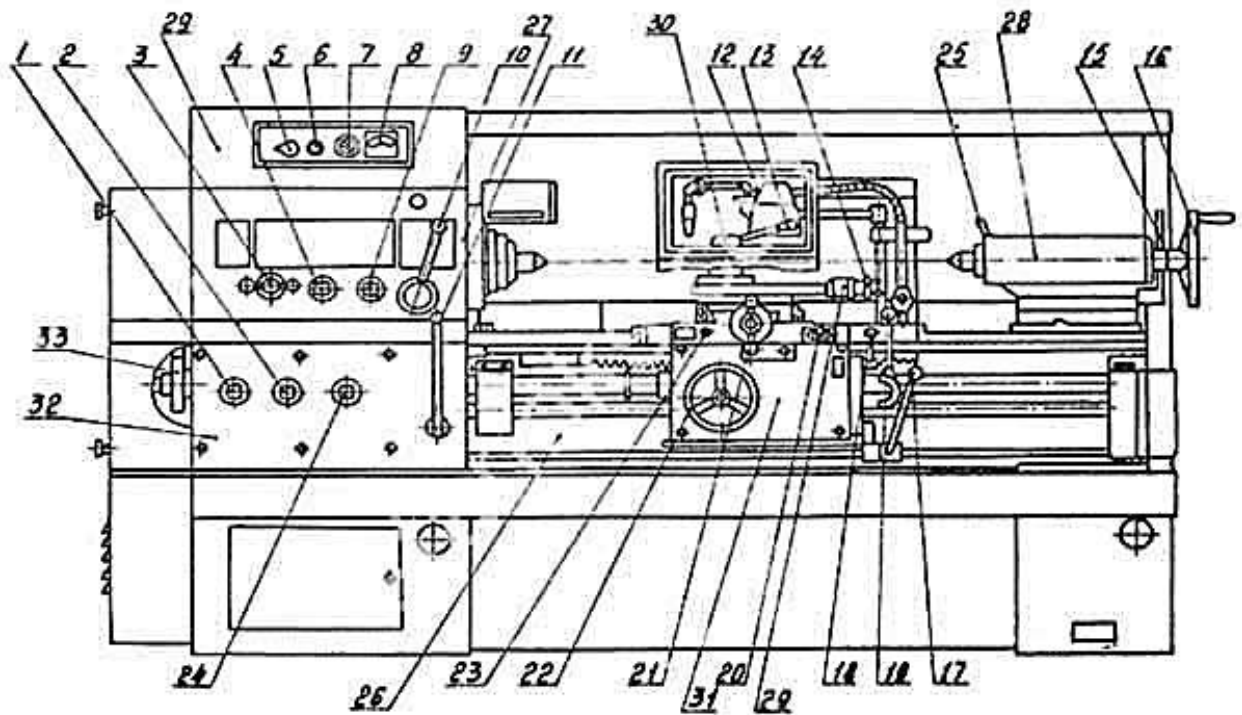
Загальний вигляд токарного верстата 16K20
